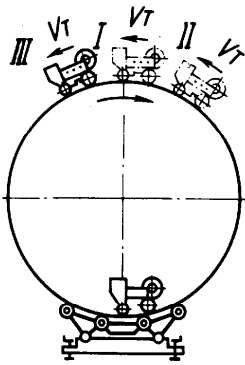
Схема сварки сферического резервуара на манипуляторе
